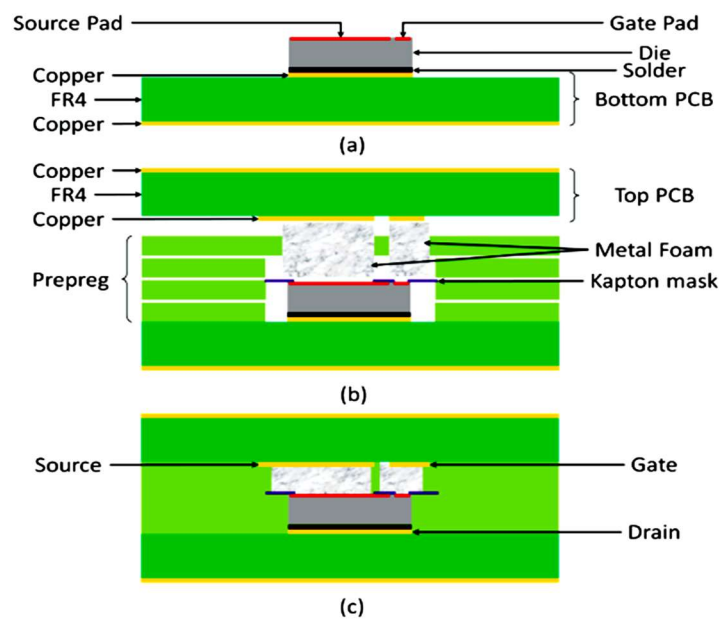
Enfouissement PCB avec mousse métallique [144]
